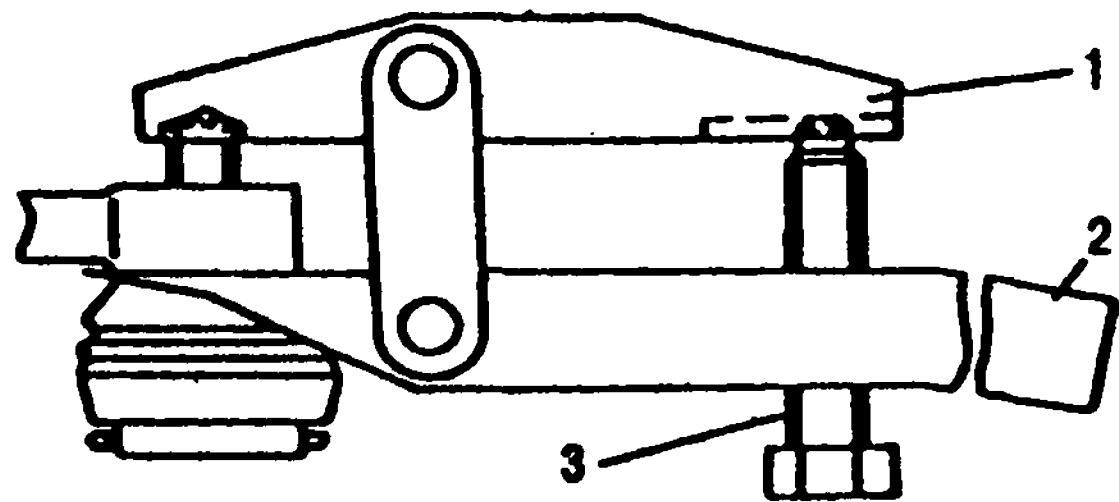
Выпрессовка пальца шарового шарнира из поворотных рычагов и бобышек тяги сошки съемником: 1 и 2 - рычаги; 3 - болт
